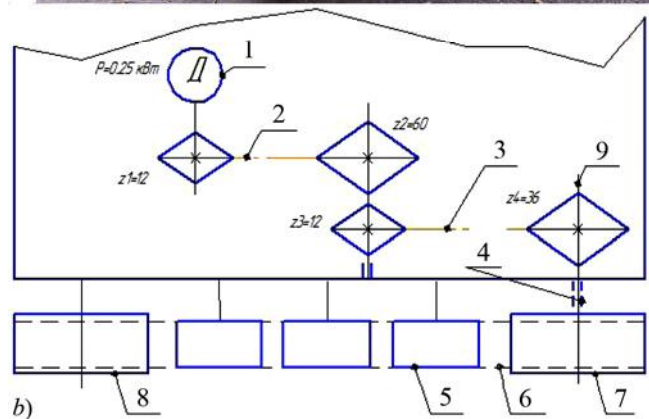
Малий мобільний робот з електромеханічною трансмісією та її розрахункова схема / Small mobile robot with electromechanical transmission and its calculation scheme: 1 – електродвигун / electric motor; 2, 3 – ланцюгова передача / gears; 4 – підшипники / bearings; 5 – катки / rollers; 6 – гусениця / caterpillar; 7 – ведуча зірочка / driven sprocket; 8 – ведена зірочка / slave sprocket; 9 – вал / shaft
